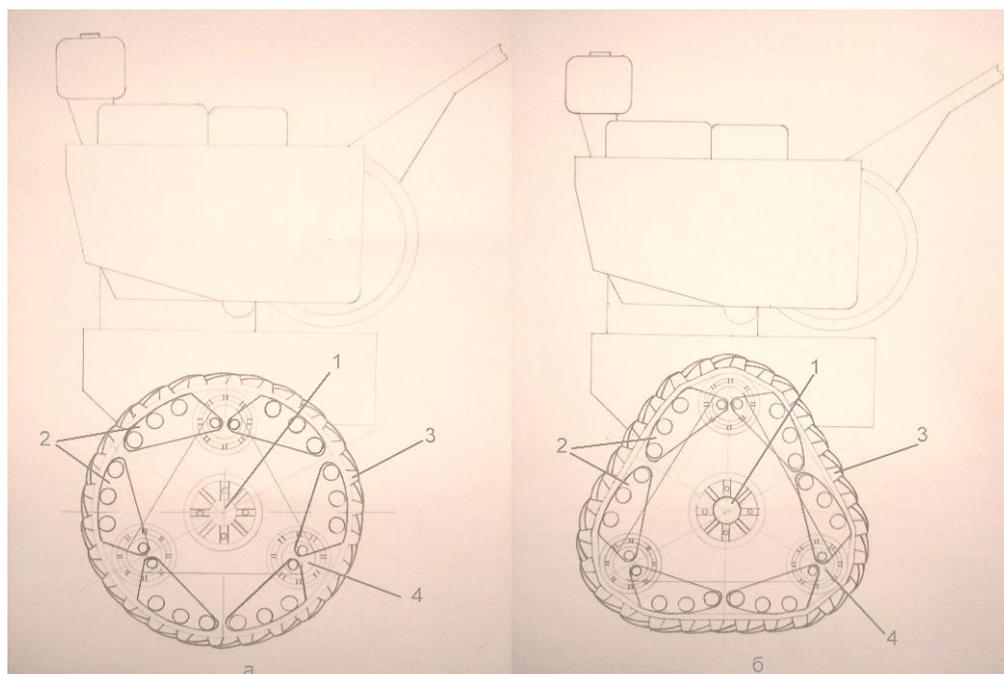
Общий вид конструкции: агрегат с мотоблоком
